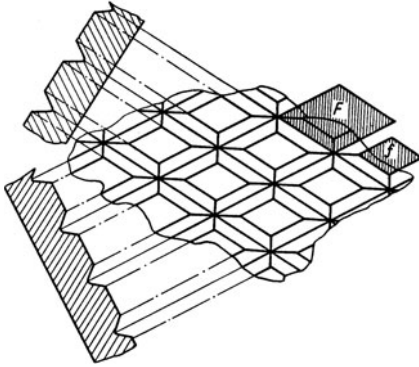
In eine Flachstanzplatte eingehobeltes oder eingefrästes Muster
